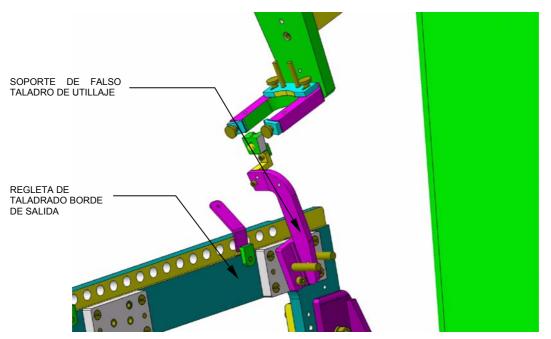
Detalle del posicionador de la costilla de cierre superior.
